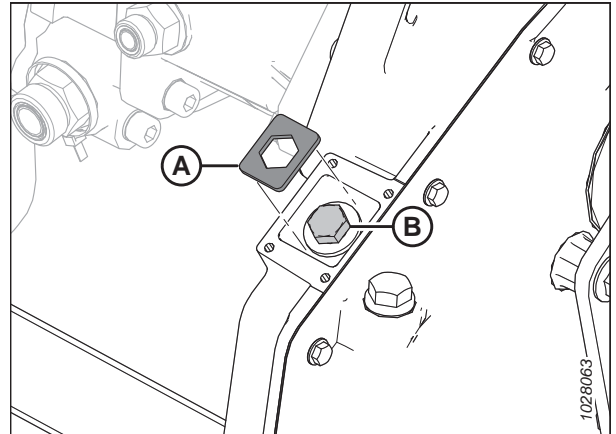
Hauptgetriebe mit Kettenspanner
